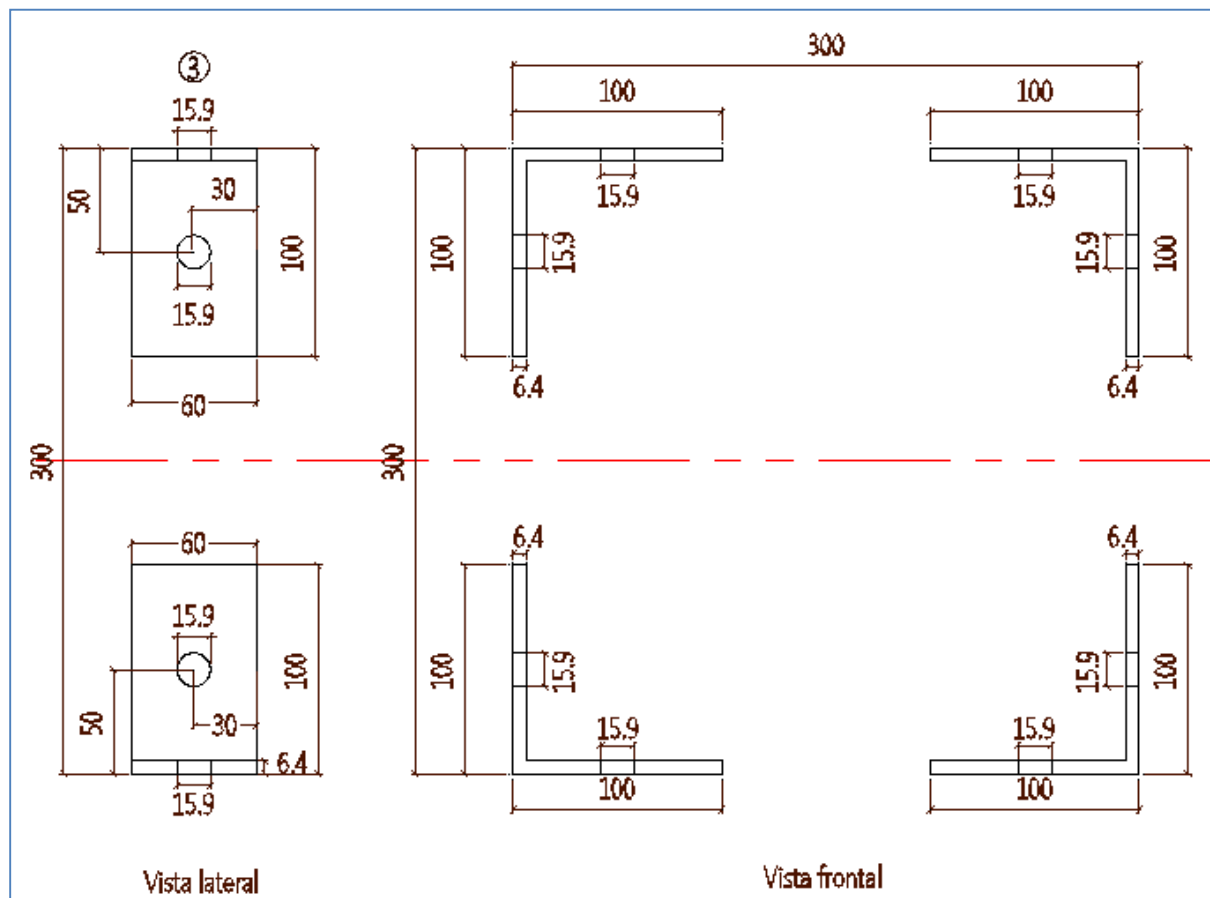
Detalle despiece pieza No.3 modelo 1 corte.
